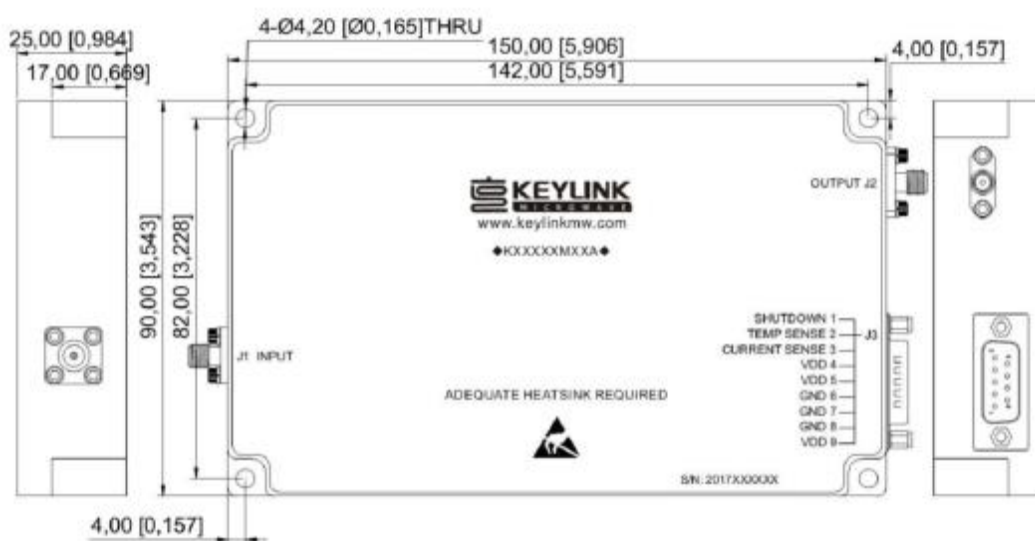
Внешний вид PC модуля KB002052M50A с указанием габаритных размеров
